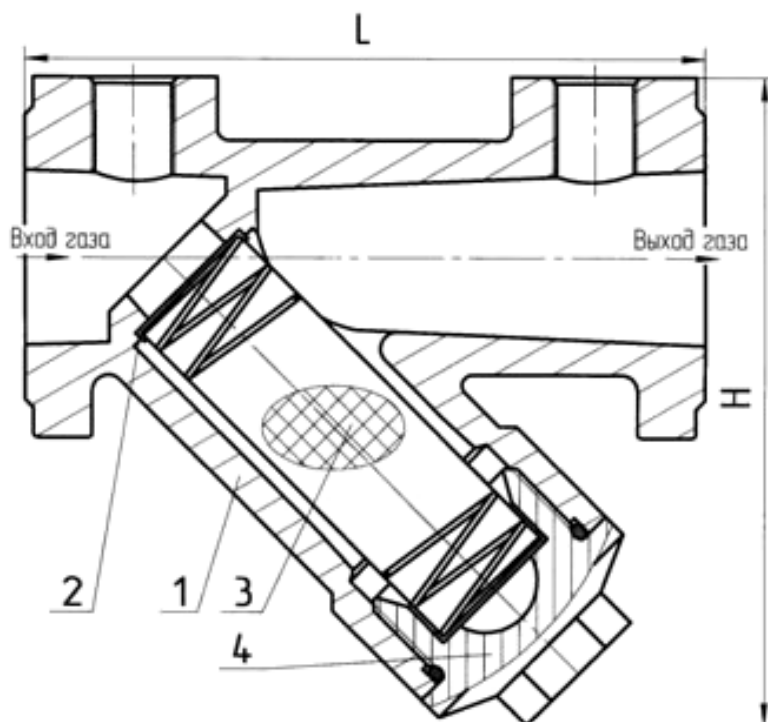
Фильтр сетчатый ФС: 1 – корпус; 2 – кассета; 3 – сетка; 4 – пробка; 5 – штуцеры
